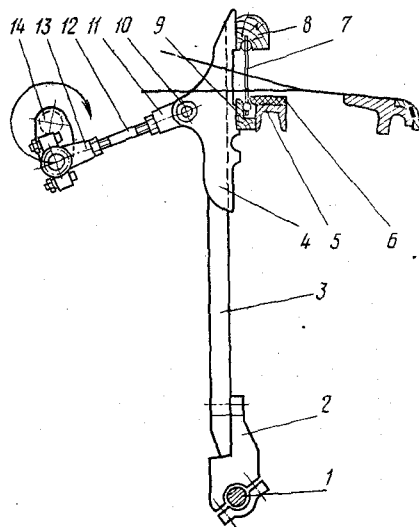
Батанный механизм автоматического станка АТ-100-5М
